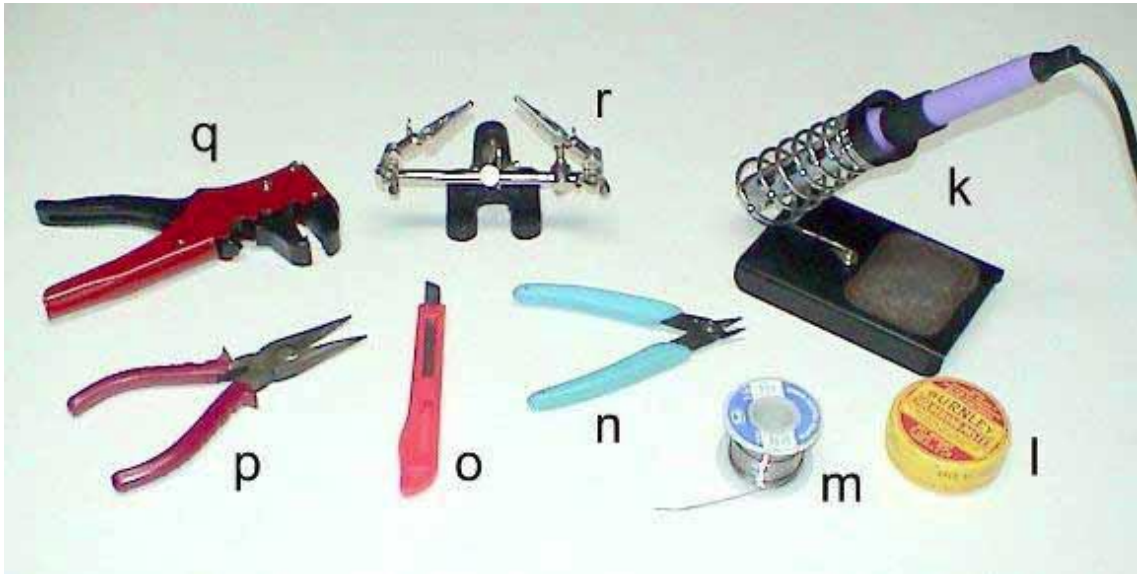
HERRAMIENTAS Y MATERIALES PARA SUELDA
